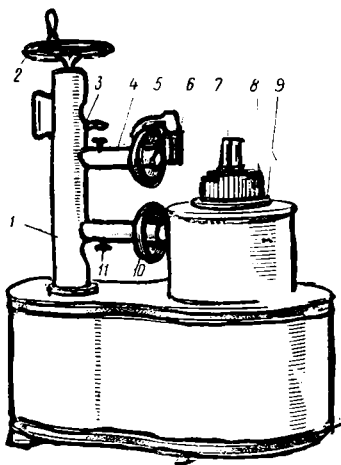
Стенд для монтажа и демонтажа шин легковых автомобилей
